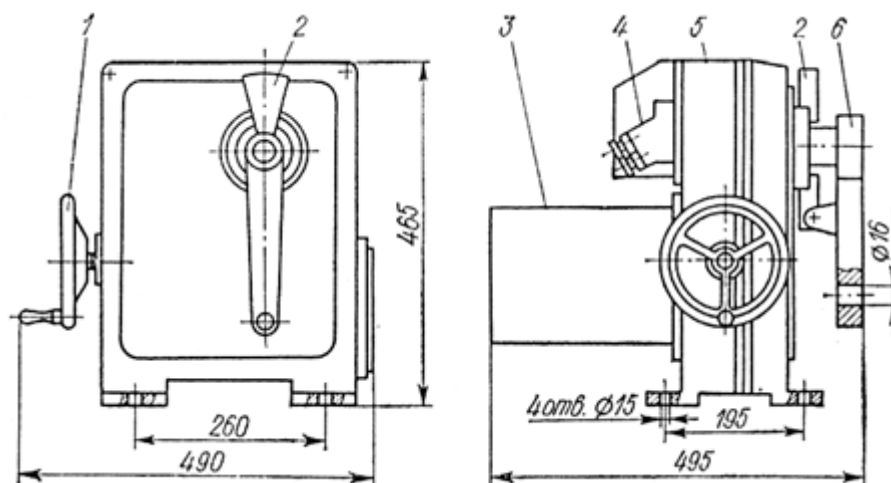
Загальний вигляд механізму МЕВ-250:
